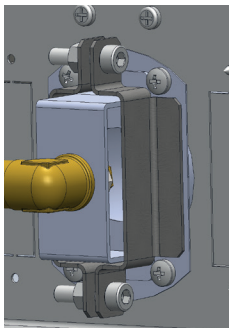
El obturador de aire del quemador del horno (1 – se compone de dos chapas fijadas con tornillos)
